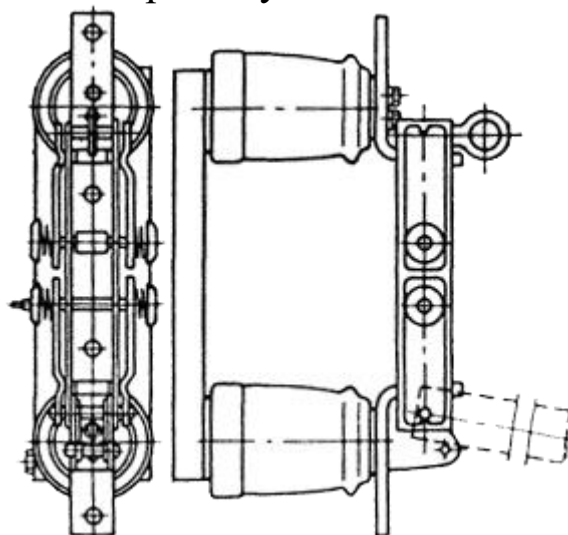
Разъединитель однополюсный РВО-10/600
